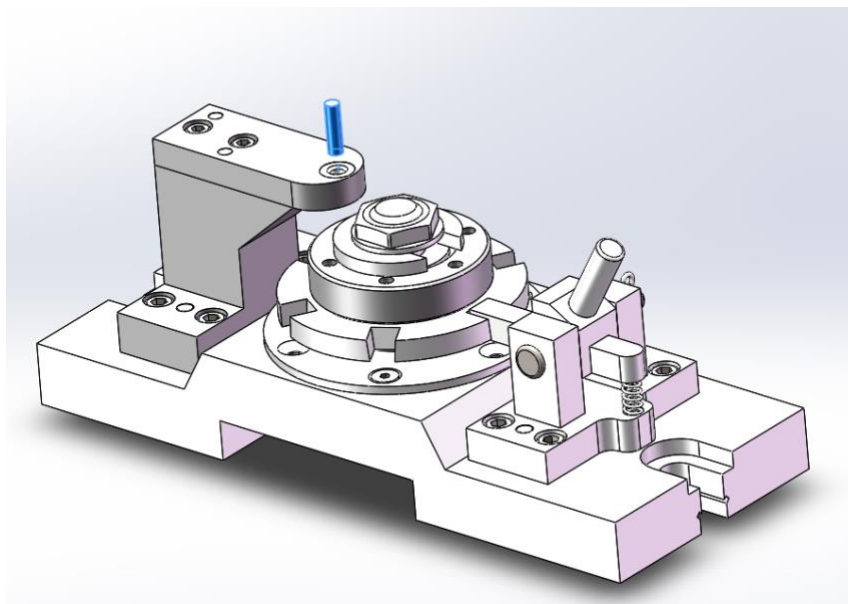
Компоновка (общий вид) приспособления показан на чертеже. (3D)
